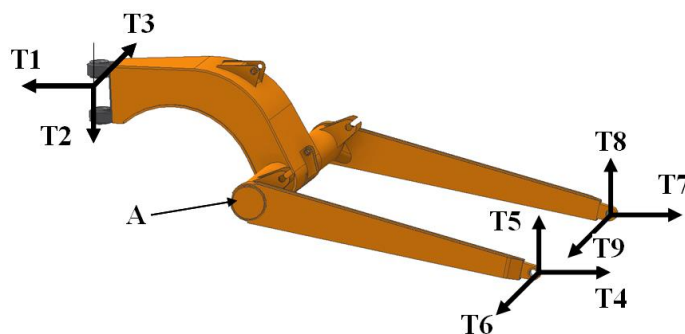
Розрахункова схема тягової рами напівпричіпного скрепера
